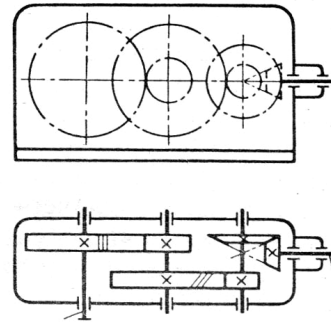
Коническо-цилиндрический трехступенчатый горизонтальный редуктор (КЦ2)
